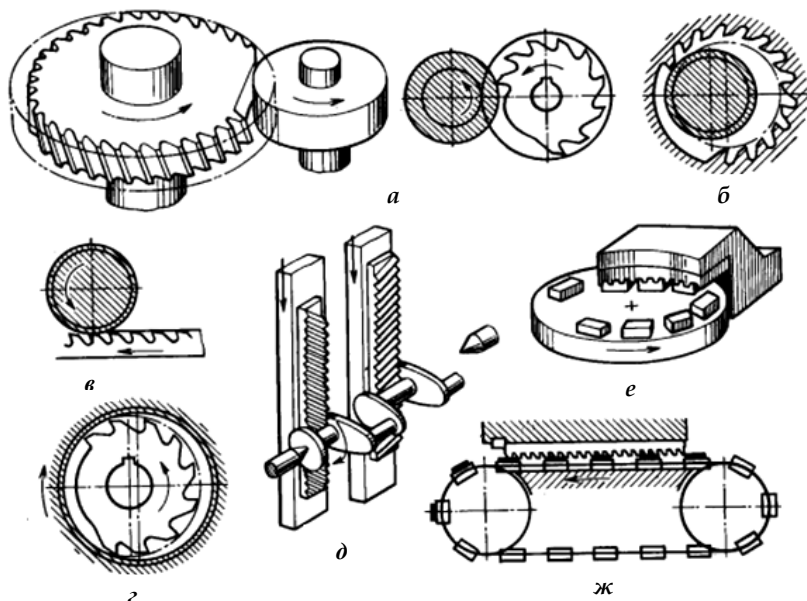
Обработка заготовок дисковыми (а) и (б), плоскими (в) протяжками, внутренних поверхностей (г), шеек коленчатых валов (д), неподвижными протяжками с помощью приспособлений карусельного (е) и цепного (ж) типов
